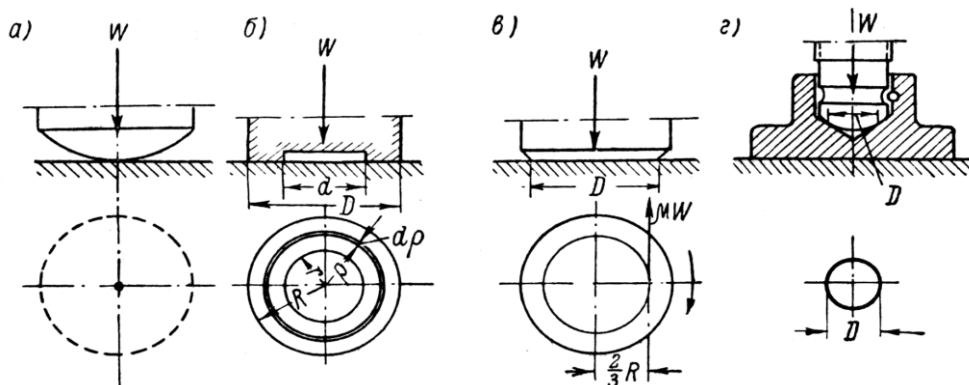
Схеми для розрахунку гвинтових механізмів різних конструкцій
